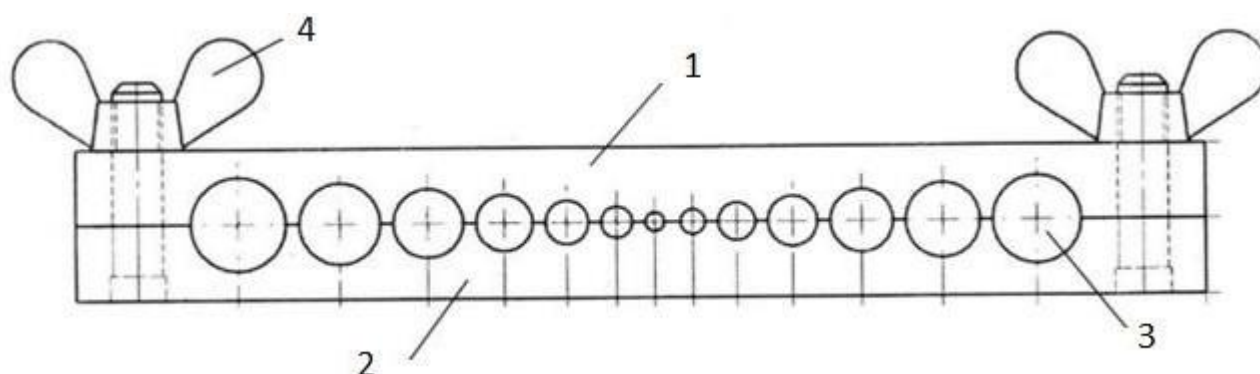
Схема пресс-формы: 1 – верхняя плита, 2 – нижняя плита, 3 – каналы плит полуцилиндрической формы, 4 – гайки-барашки для соединения плит между собой
